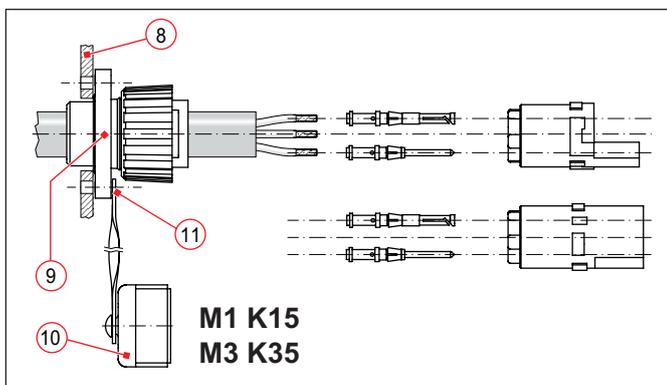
Montagebeispiel für Stecker mit Flansch an eine Montagewand
